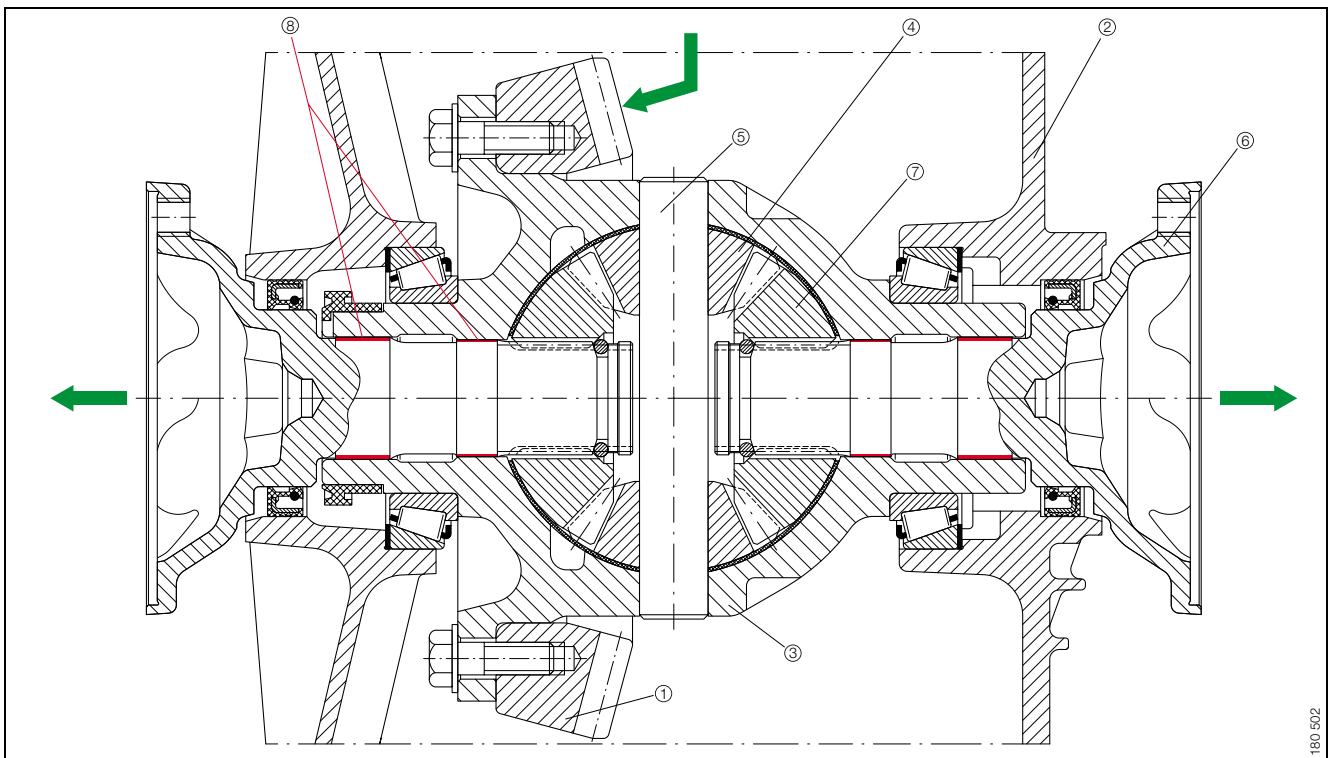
· Differentialgetriebe mit gleitgelagerten Flanschwellen – konstruktive Ausführung
